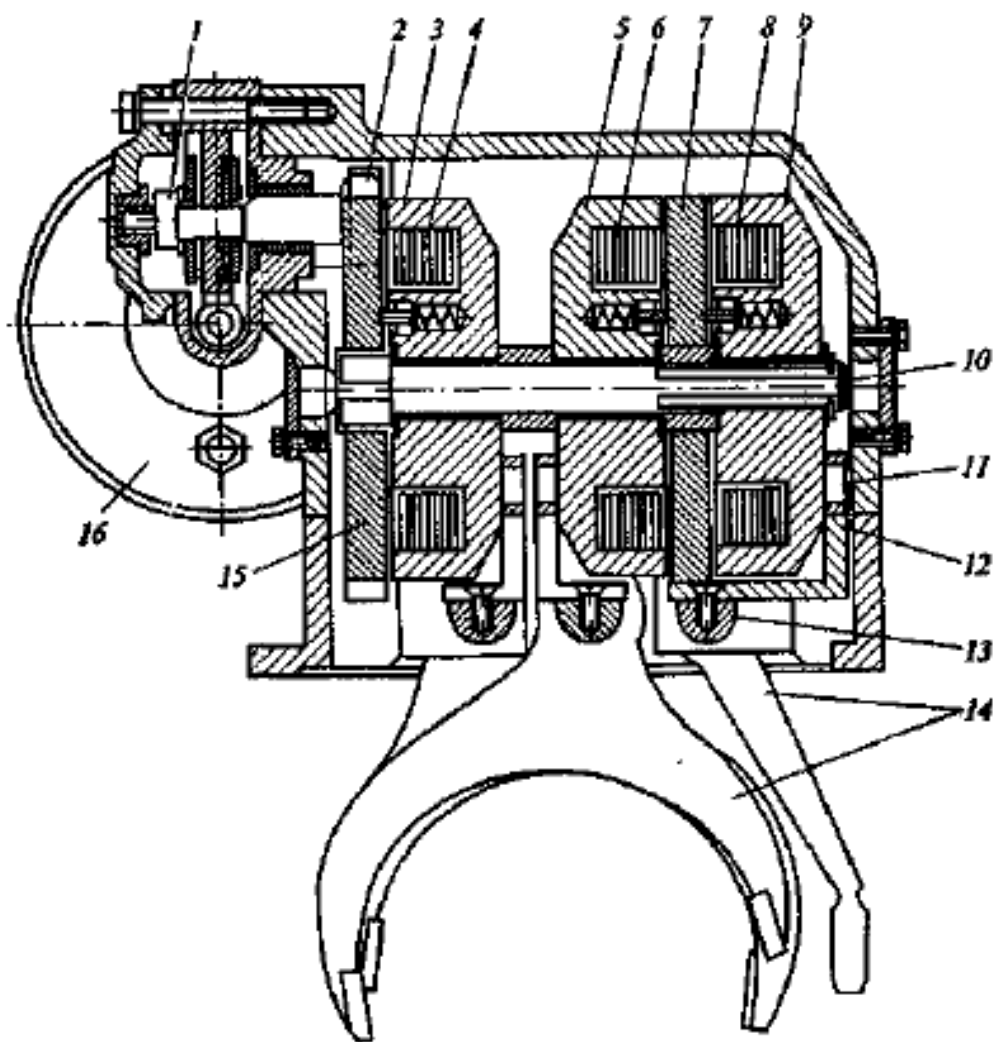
Электромеханический исполнительный механизм переключения передач (разработка НАМИ): 1 – редуктор; 2 и 15 – шестерни; 3, 5 и 9 – муфты; 4, 6 и 8 – обмотки электромагнитов; 7 – диск; 10 – ведущий вал; 11 – палец; 12 – пластина; 13 – ползун; 14 – вилки; 16 – электродвигатель
